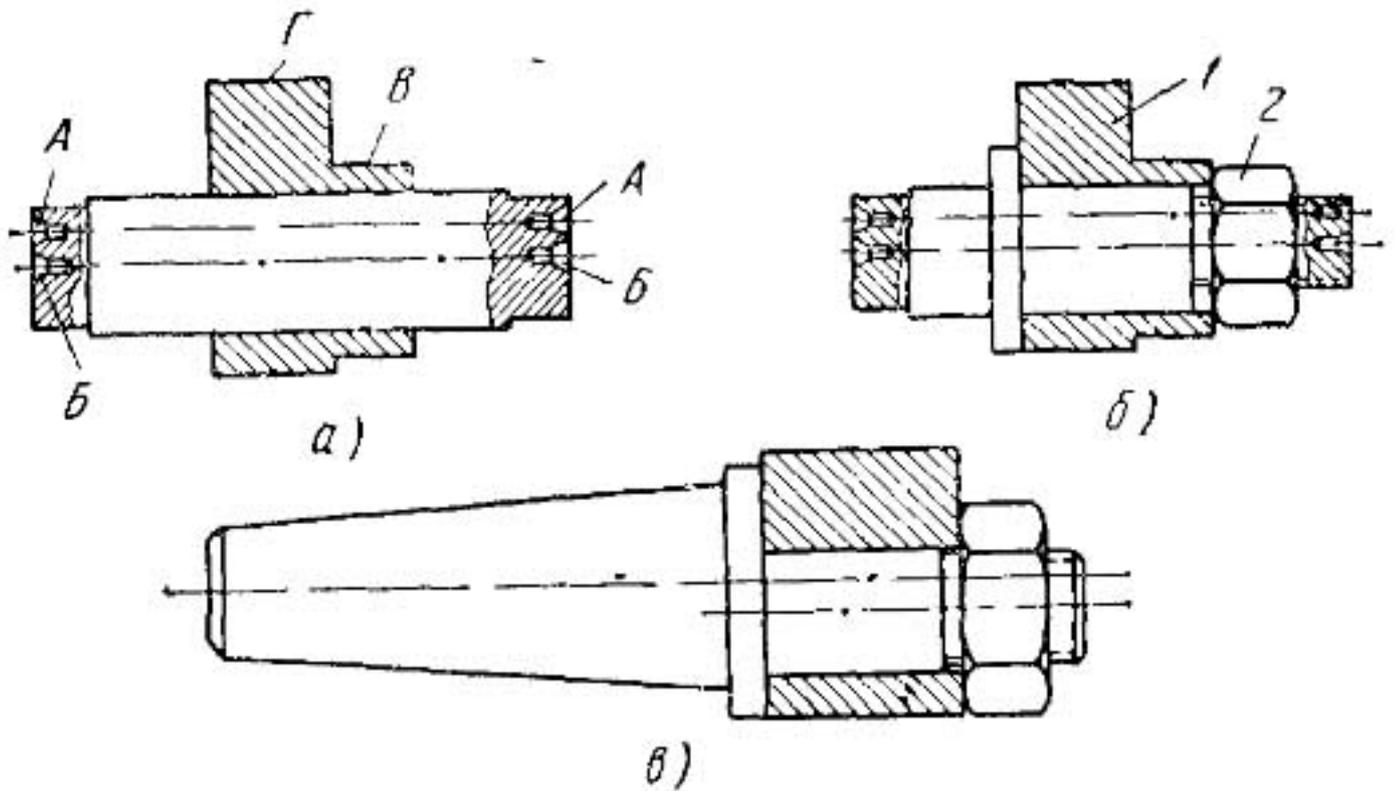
Оправки для обтачивания эксцентриковых деталей:
